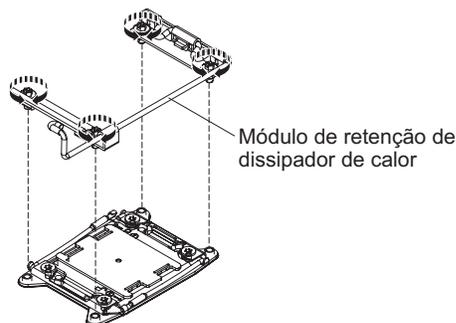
Instalação do módulo de retenção de dissipador de calor do dissipador de calor
